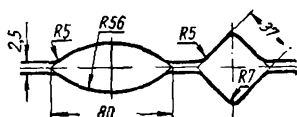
Размер ручьев при вальцовке круглой заготовки
